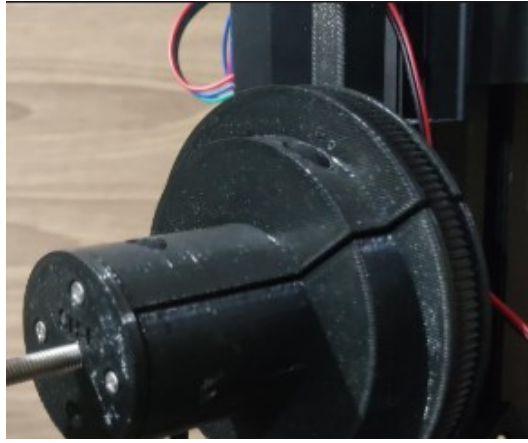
Ajuste del bobinado inicial. Fuente propia.
